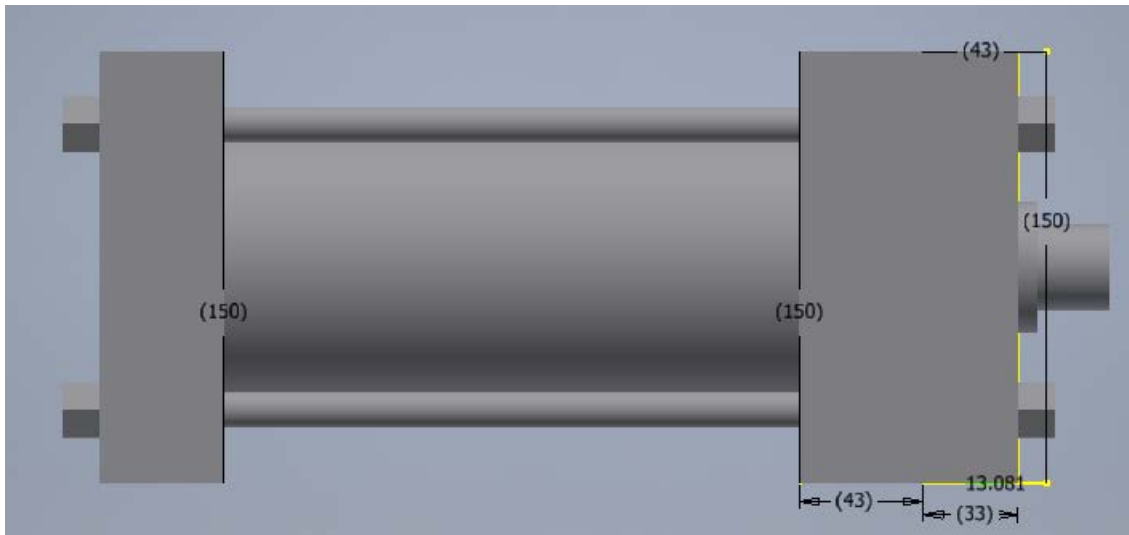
Ensamble del cilindro-pistón en vista de perfil
